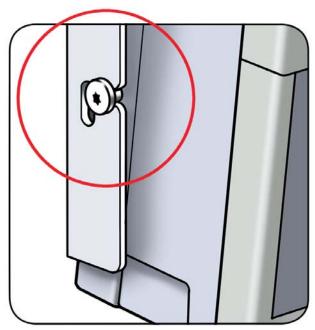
Einführung der Schrauben in die Schlitze – Detailansicht
